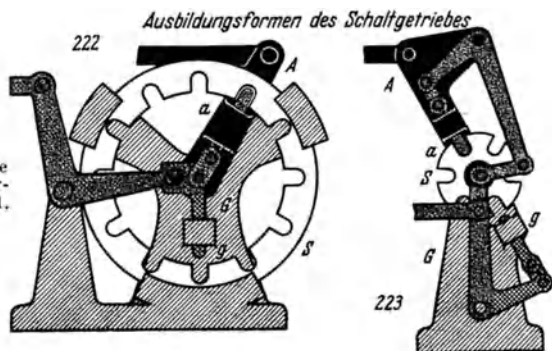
u. 223. Formschlüssige Schaltgetriebe zu Schaltwerken entsprechend Abb. 221.
